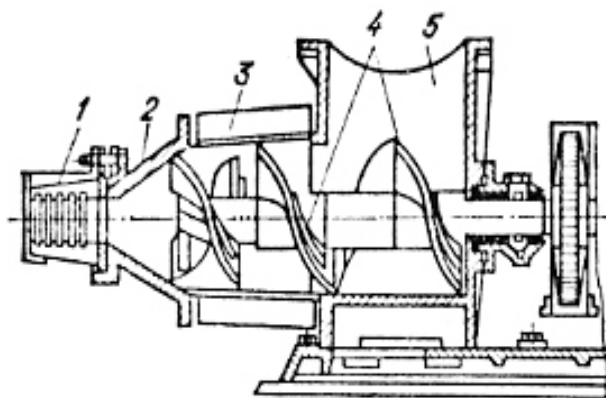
Ленточный шнековый пресс: 1 – мундштук; 2 – головка прессы; 3 – цилиндр прессы; 4 – лопасти шнека; 5 – воронка
